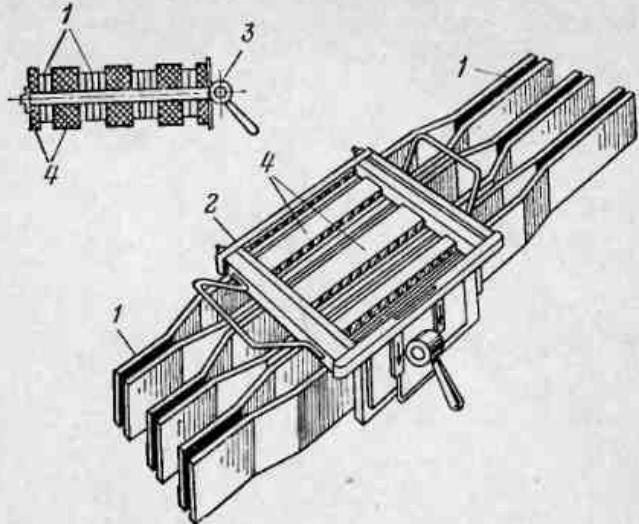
Кондуктор для сварки стыков шин.
